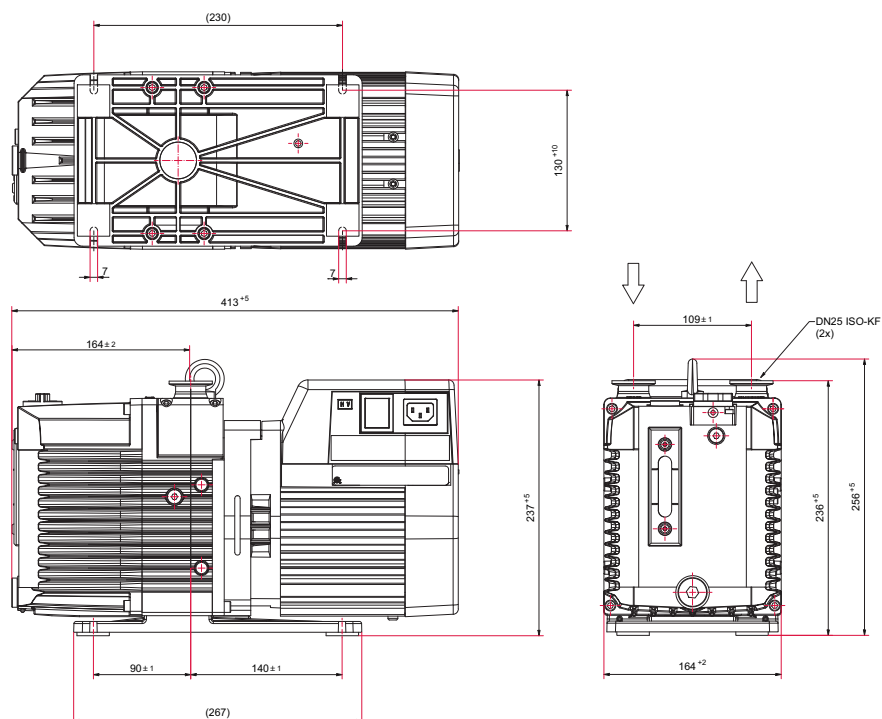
Dimensions DuoVane 6 avec moteur monophasé
